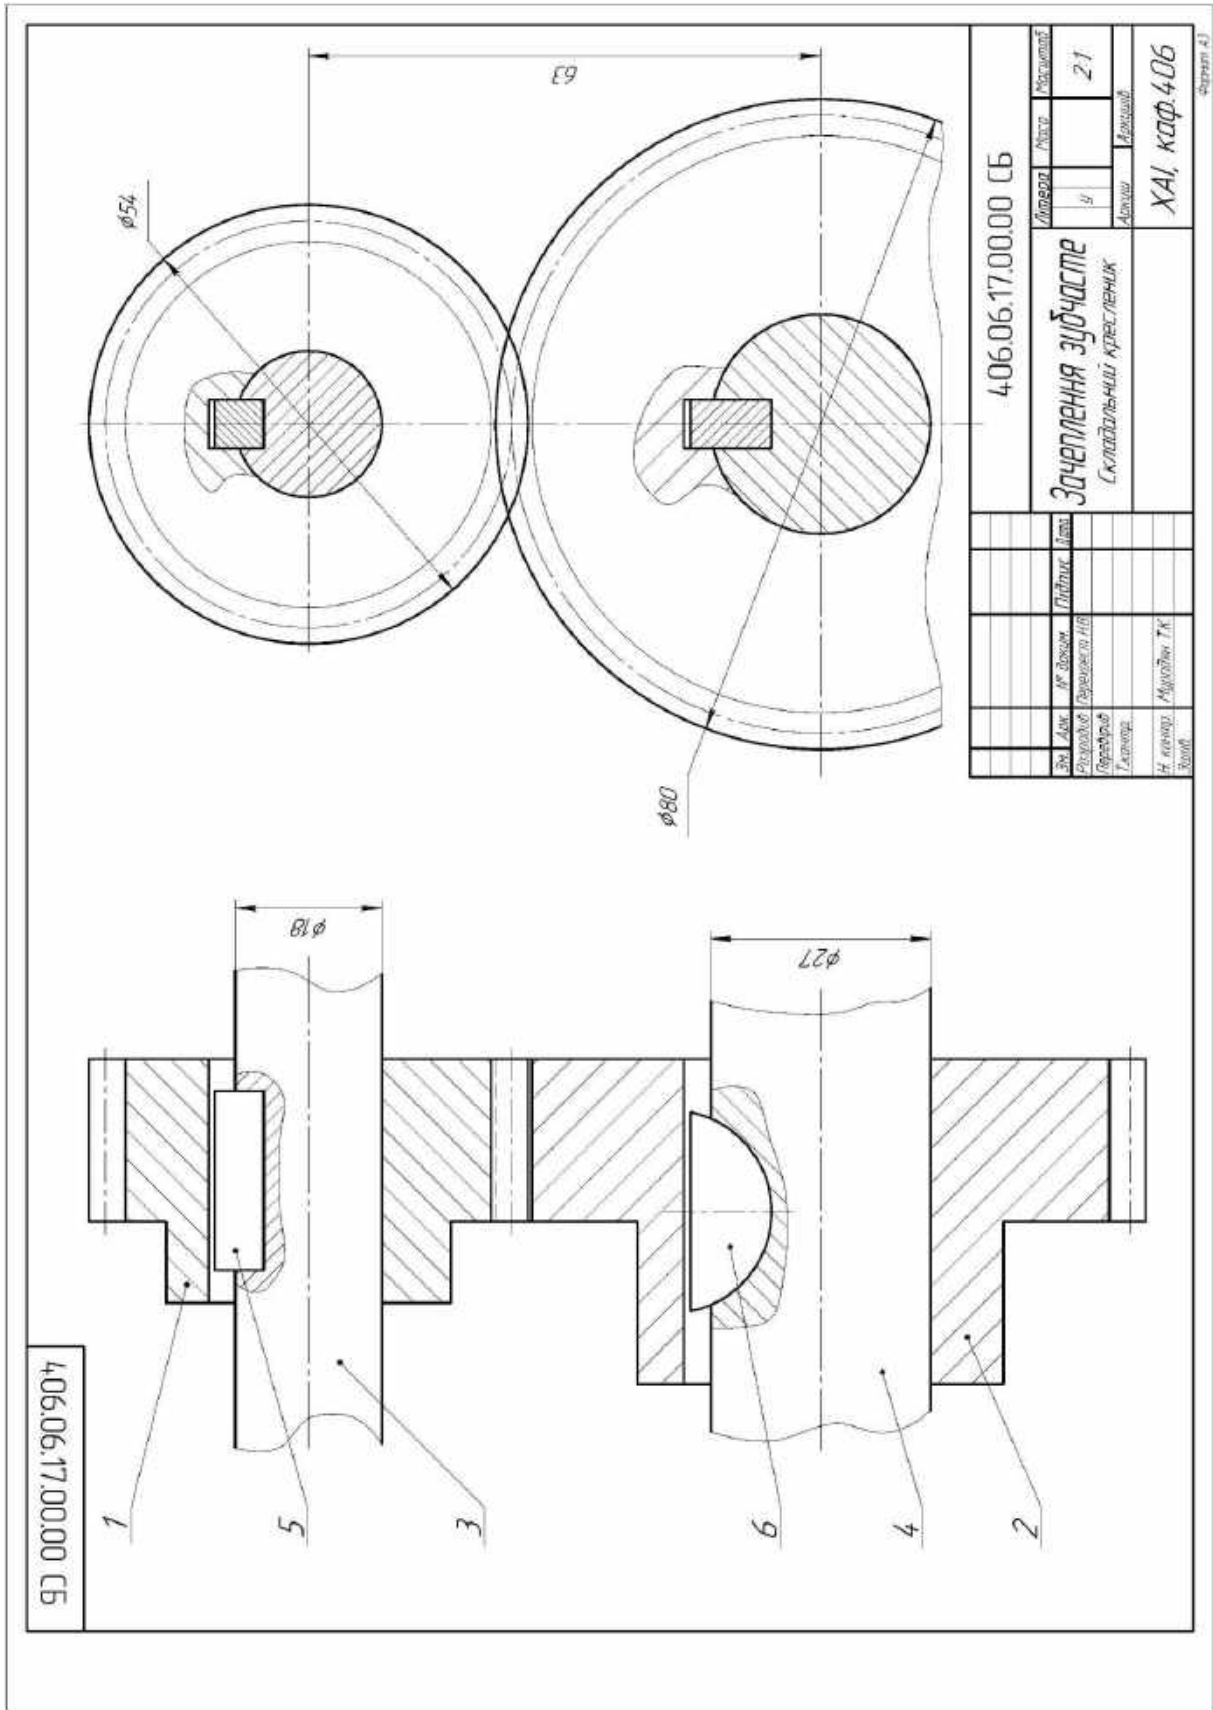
Складальний кресленник зубчастого зачеплення зі шпонковими з'єднаннями
